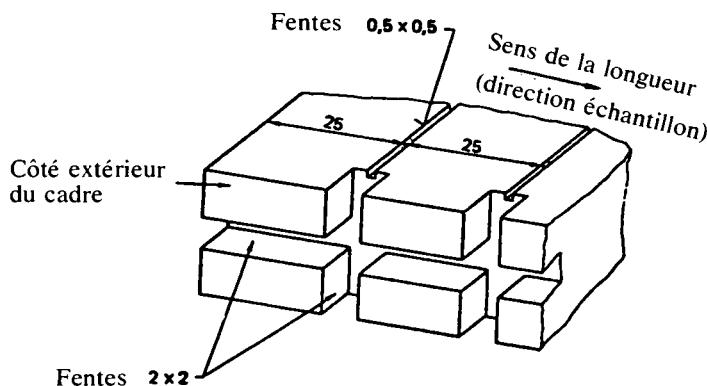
Exemple de section du cadre en forme de U, partie inférieure prévue pour équipement avec fils de support
